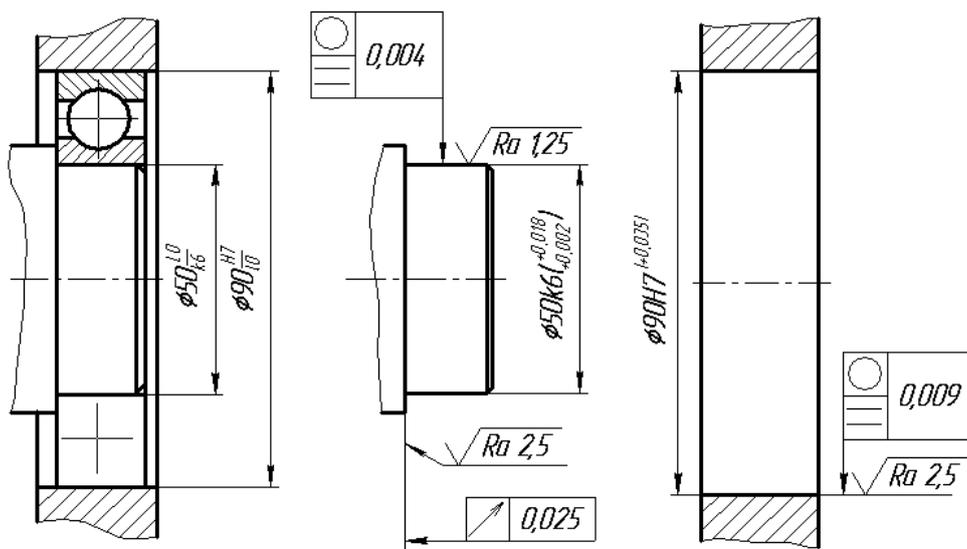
Эскиз подшипникового узла, вала и корпуса
